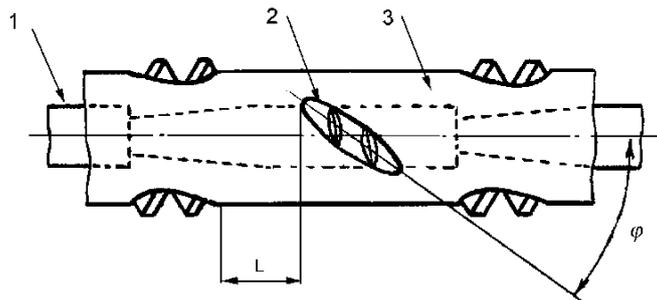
Конструкция многощеточного шпалера: 1 — клин; 2 — щетка; 3 — трубка
